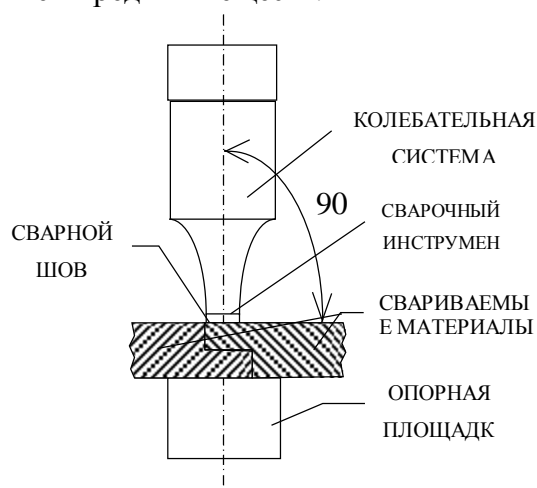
Выбор положения и угла наклона рабочего сварочного инструмента
